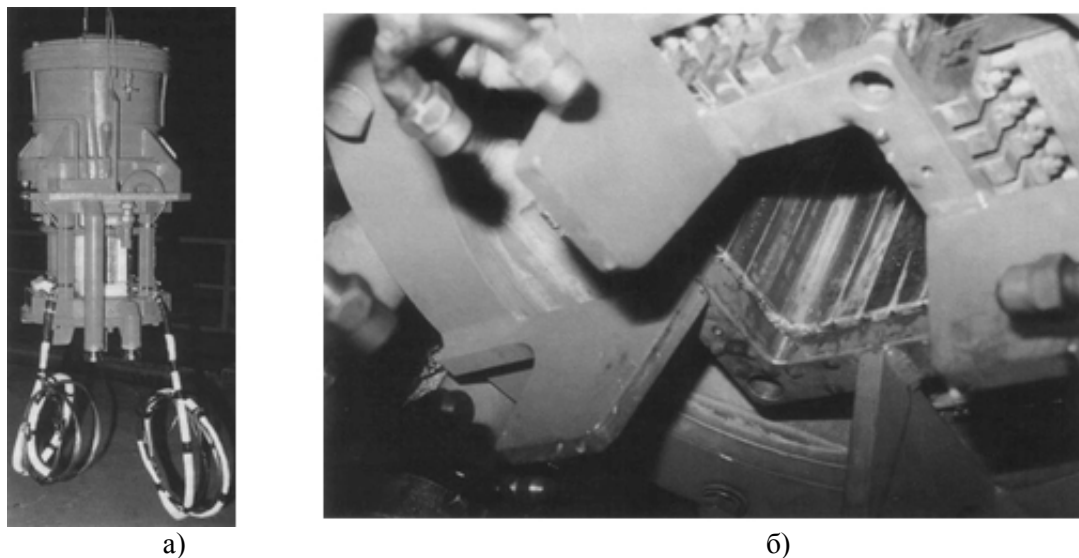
Кристаллизатора конструкции “CONVEX MOULD”.
